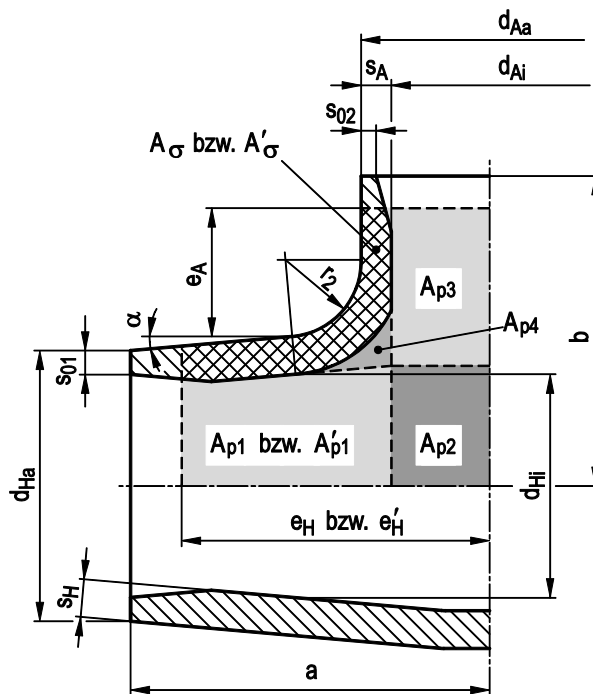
Dimensionierungsflächen für Einschweiß-T-Stück
